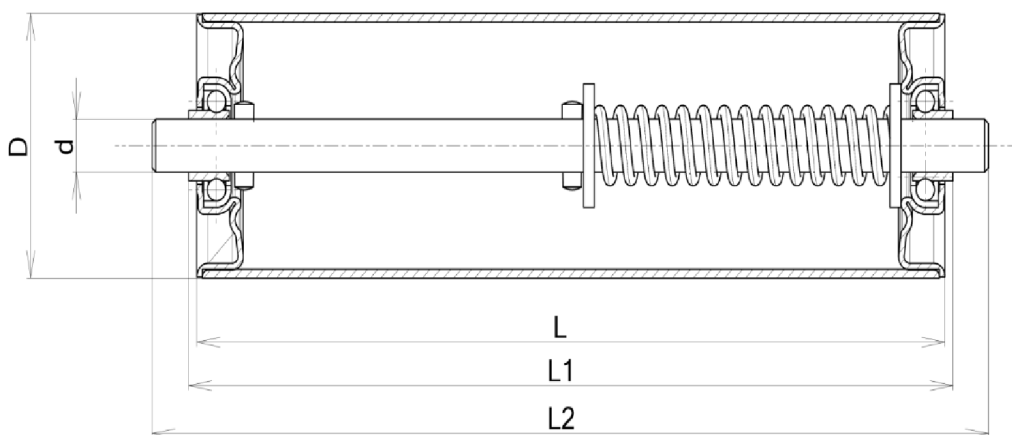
Ložisko k napínání bubnu TU 25 TF [37]
